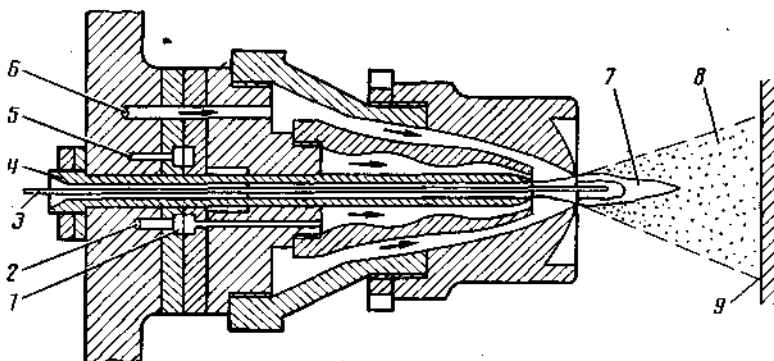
Распылительная головка аппарата для газопламенного напыления: 1— смесительная камера; 2— канал подачи кислорода; 3— проволока; 4— направляющая втулка; 5— канал подачи ацетилена; 6— канал подачи сжатого воздуха; 7— ацетилено-кислородное пламя; 8— газо-металлическая струя; 9— напыляемая поверхность
